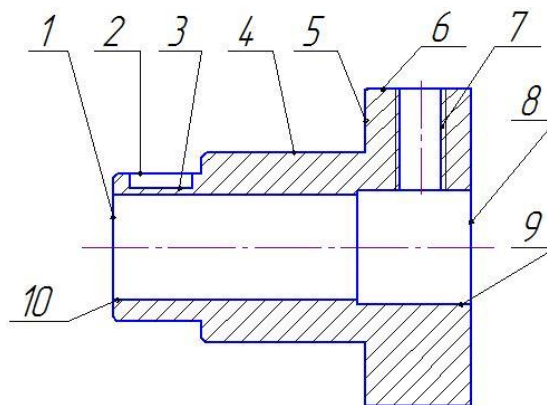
Ескіз деталі «Втулка» з позначенням поверхонь
